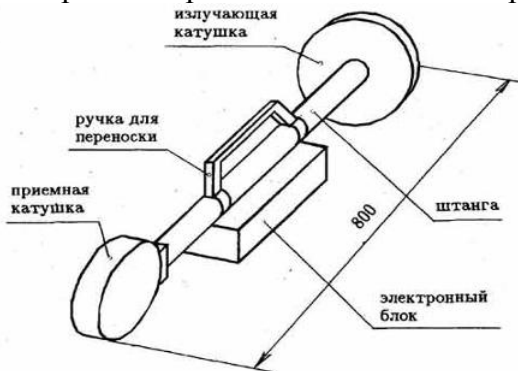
Конструкція металошукача за принципом "передача-прийом". Загальний вид.
